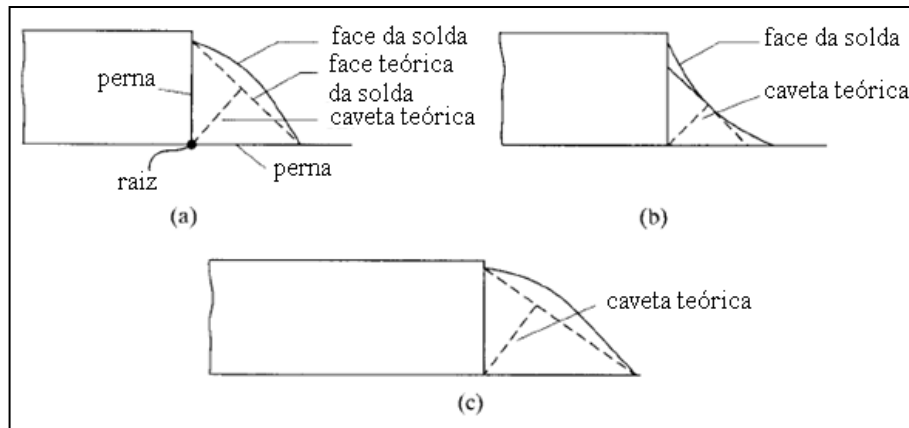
(a) Superfície convexa (b) Superfície côncava (c) Pernas desiguais do filete de solda. (Adaptado de McCormac & Csernak, 2012)
